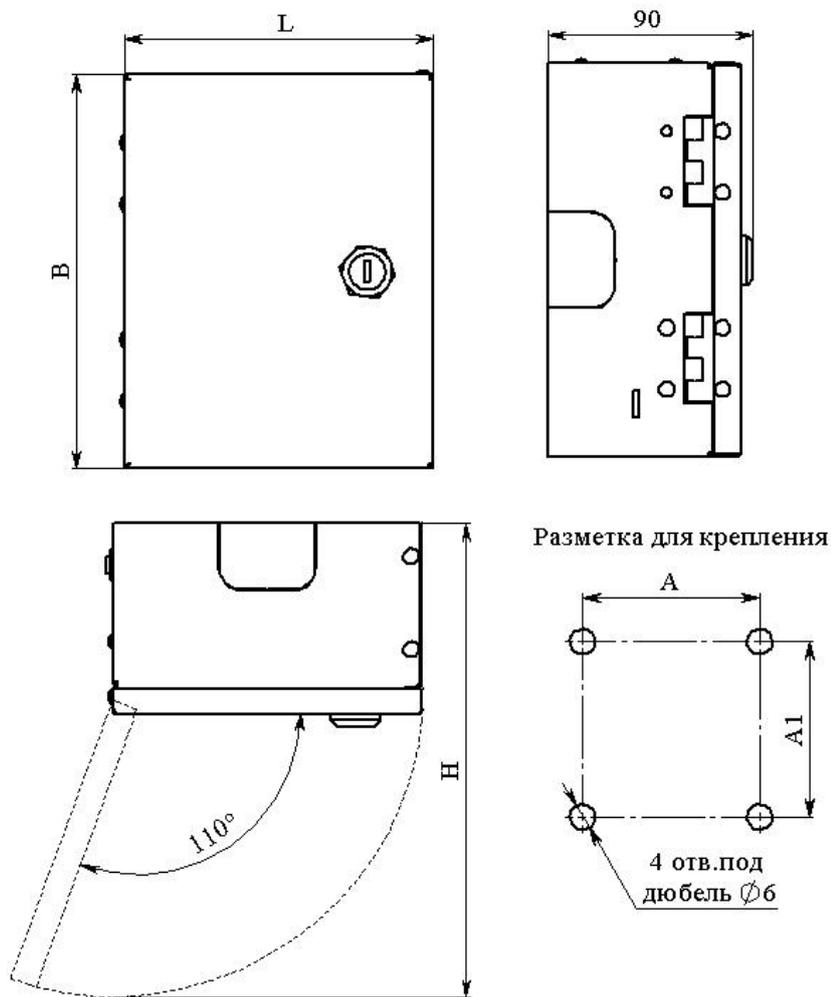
Габаритный чертеж шкафа ШРН-1М-2/30
